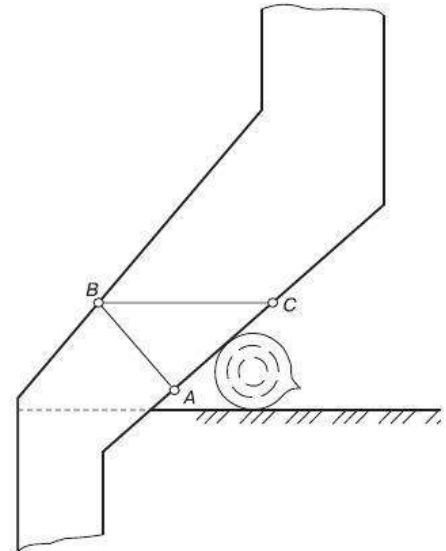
Схематичне зображення середньої частини фрезерного ножа
